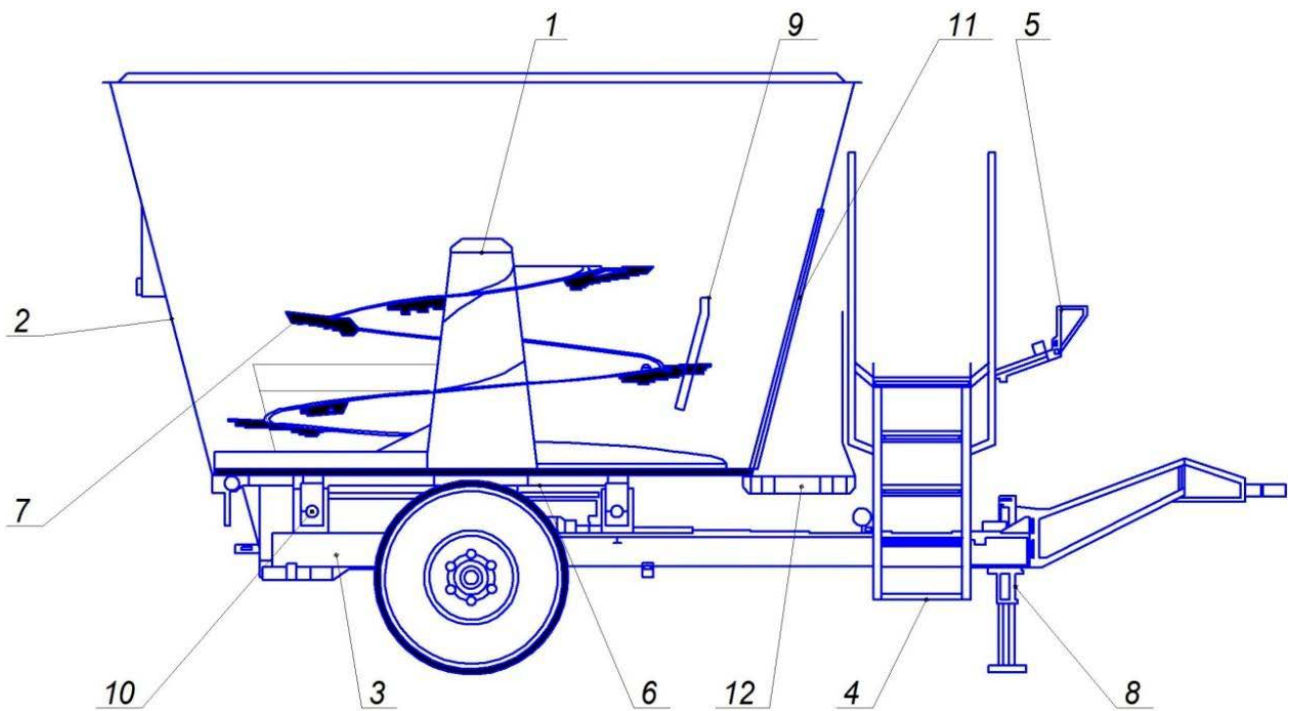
Схема комбінованого агрегату для приготування і роздавання кормів:
